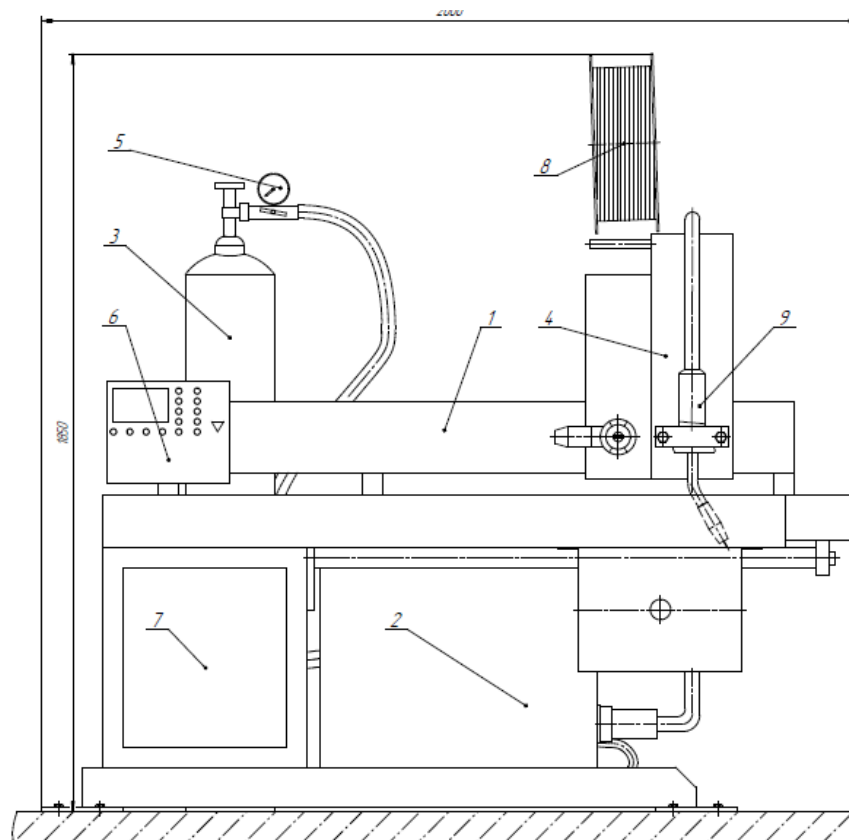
Установка для автоматичного зварювання поздовжнього шва
